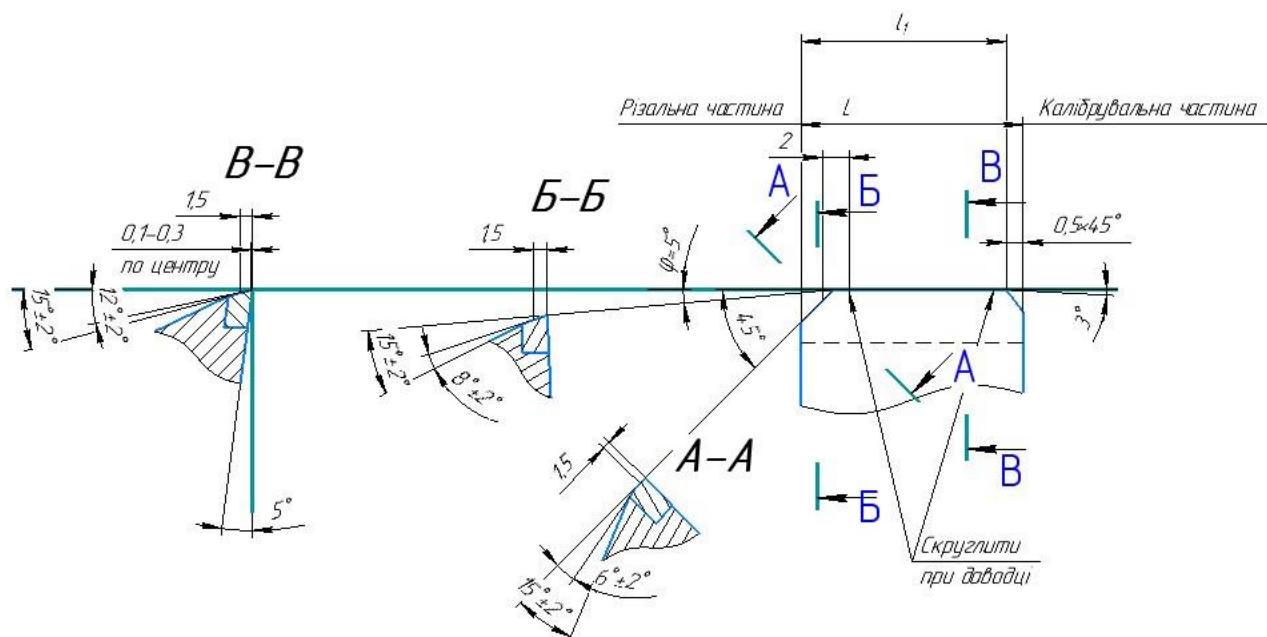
Геометричні параметри робочої частини розвертки
